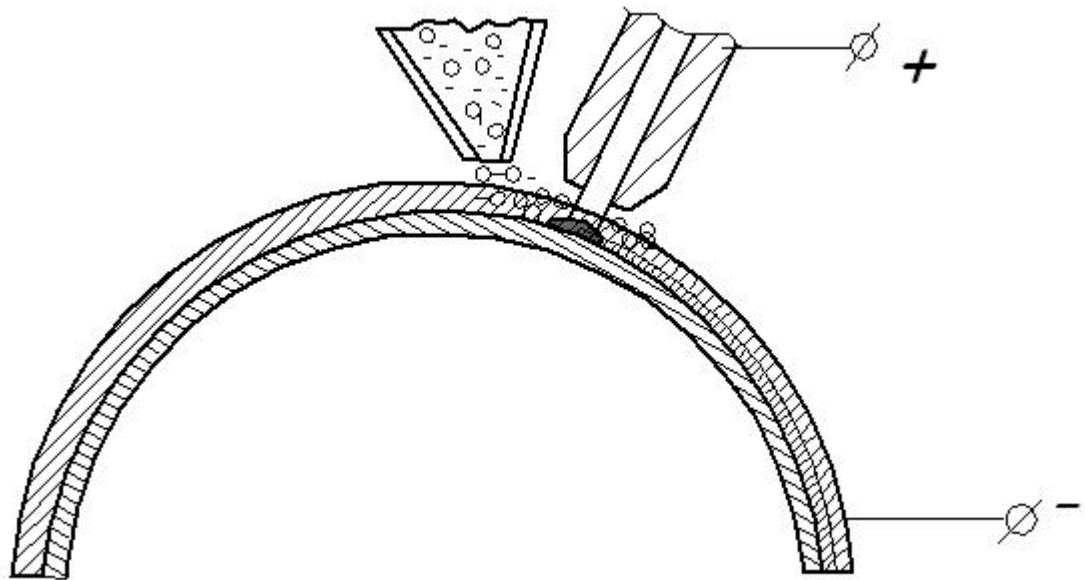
Схема автоматической сварки под слоем флюса
